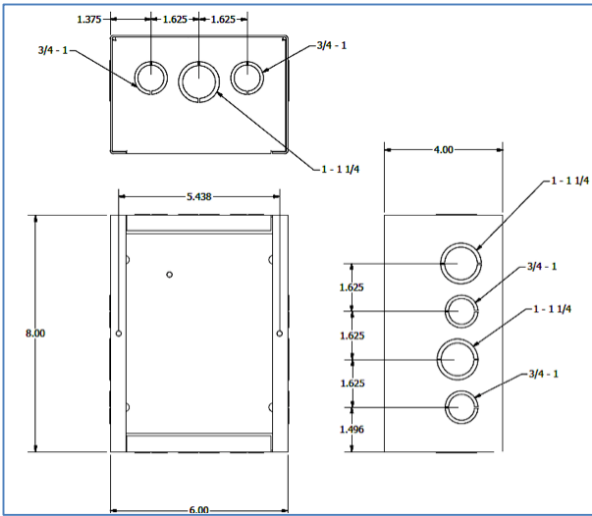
Dimensiones y Planos de Montaje de Módulo LIM
